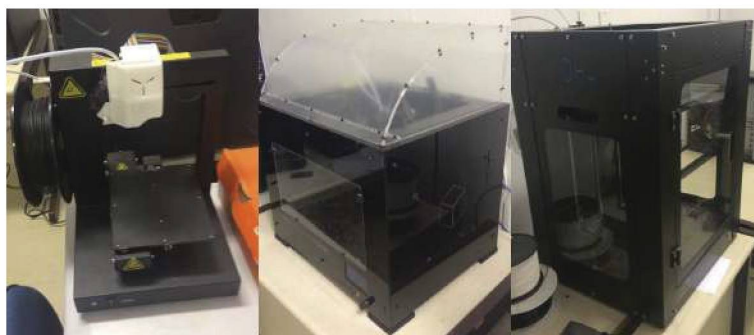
(a) Impressora UP 3D Plus (b) Impressora 3D Machine One (c) Impressora 3D Cloner DH+.
